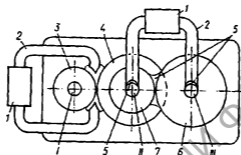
Редуктор с магнитной смазкой: I, II и III — ведущий, промежуточный и выходной валы (1 — магнитный возбудитель; 2 — полюсные наконечники; 3, 4 — зубчатые колеса из немагнитного материала; 5 — магнитная жидкость; 6, 7 — стальные зубчатые колеса)
